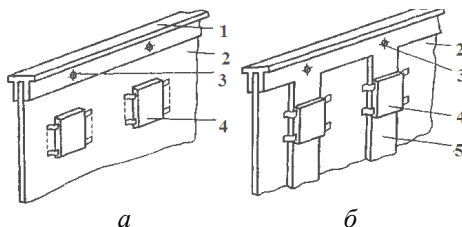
Накладки на платах: 1 – ручка; 2 – плата; 3 – кріпильний гвинт; 4 – інтегральна мікросхема; 5 – тепловідвід
